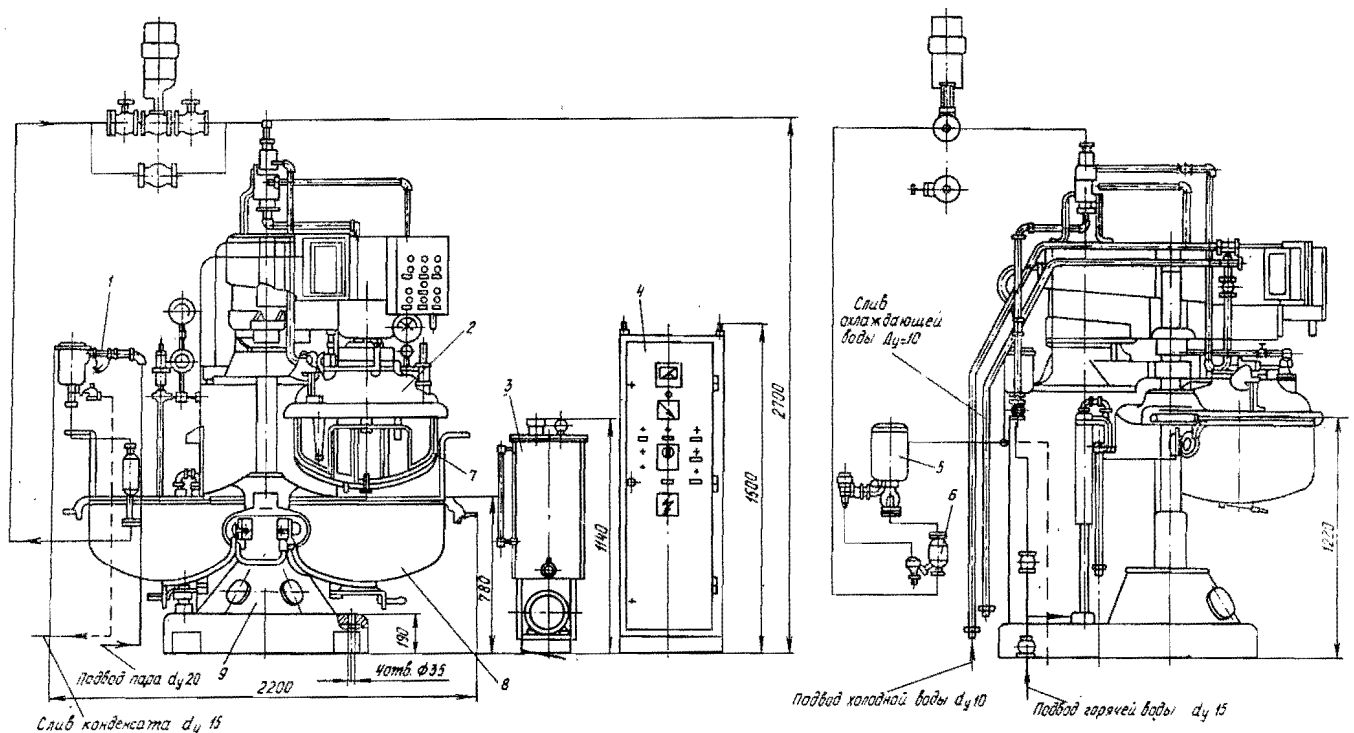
Общий вид аппарата марки Б6-ОПЕ-400 для плавления сырной массы:
